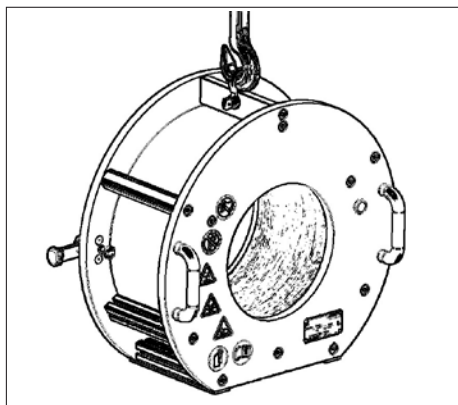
Cordas de aço não devem ser usadas para içar o aquecedor
